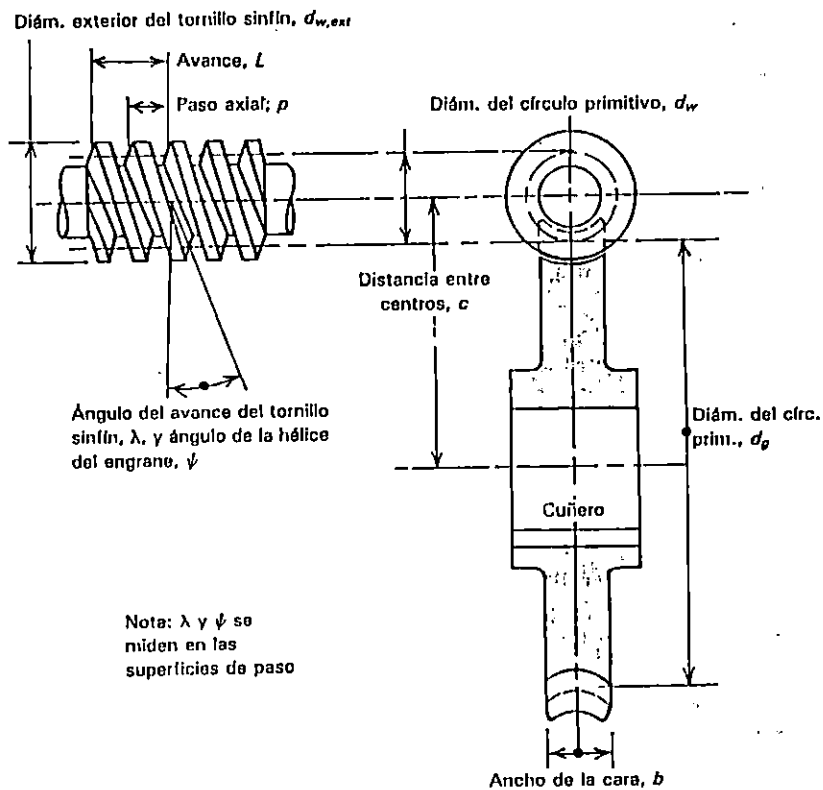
Nomenclatura del engranaje del tornillo sinfín mostrado para un tornillo con doble cuerda y engrane evolvente. /13/
